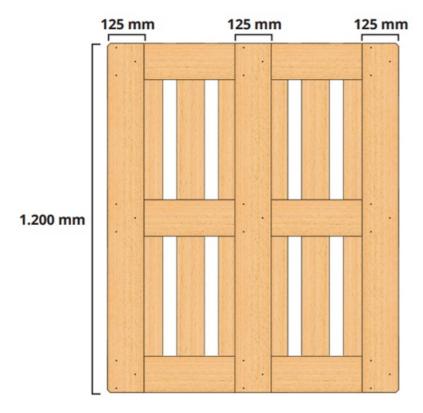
Esquema de vista inferior de um pallet com tábuas inferiores com 1200 mm de comprimento e 125 mm de largura.
